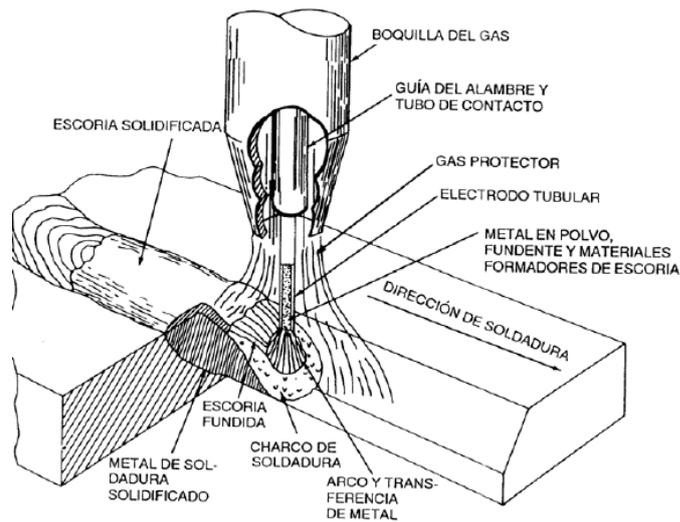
Soldadura FCAW protegida con gas
